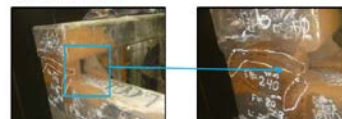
Perforadora Pitviper 271 y detalle de fisuras detectadas
